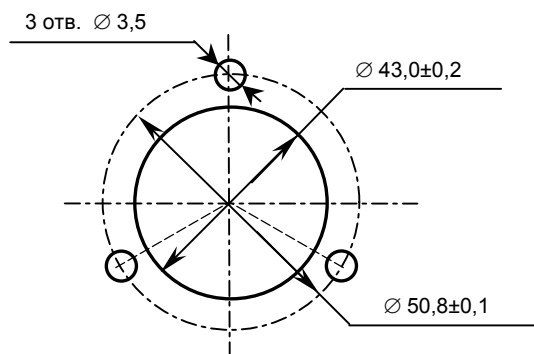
Установочные размеры штурвала ZBG-5-003-100
